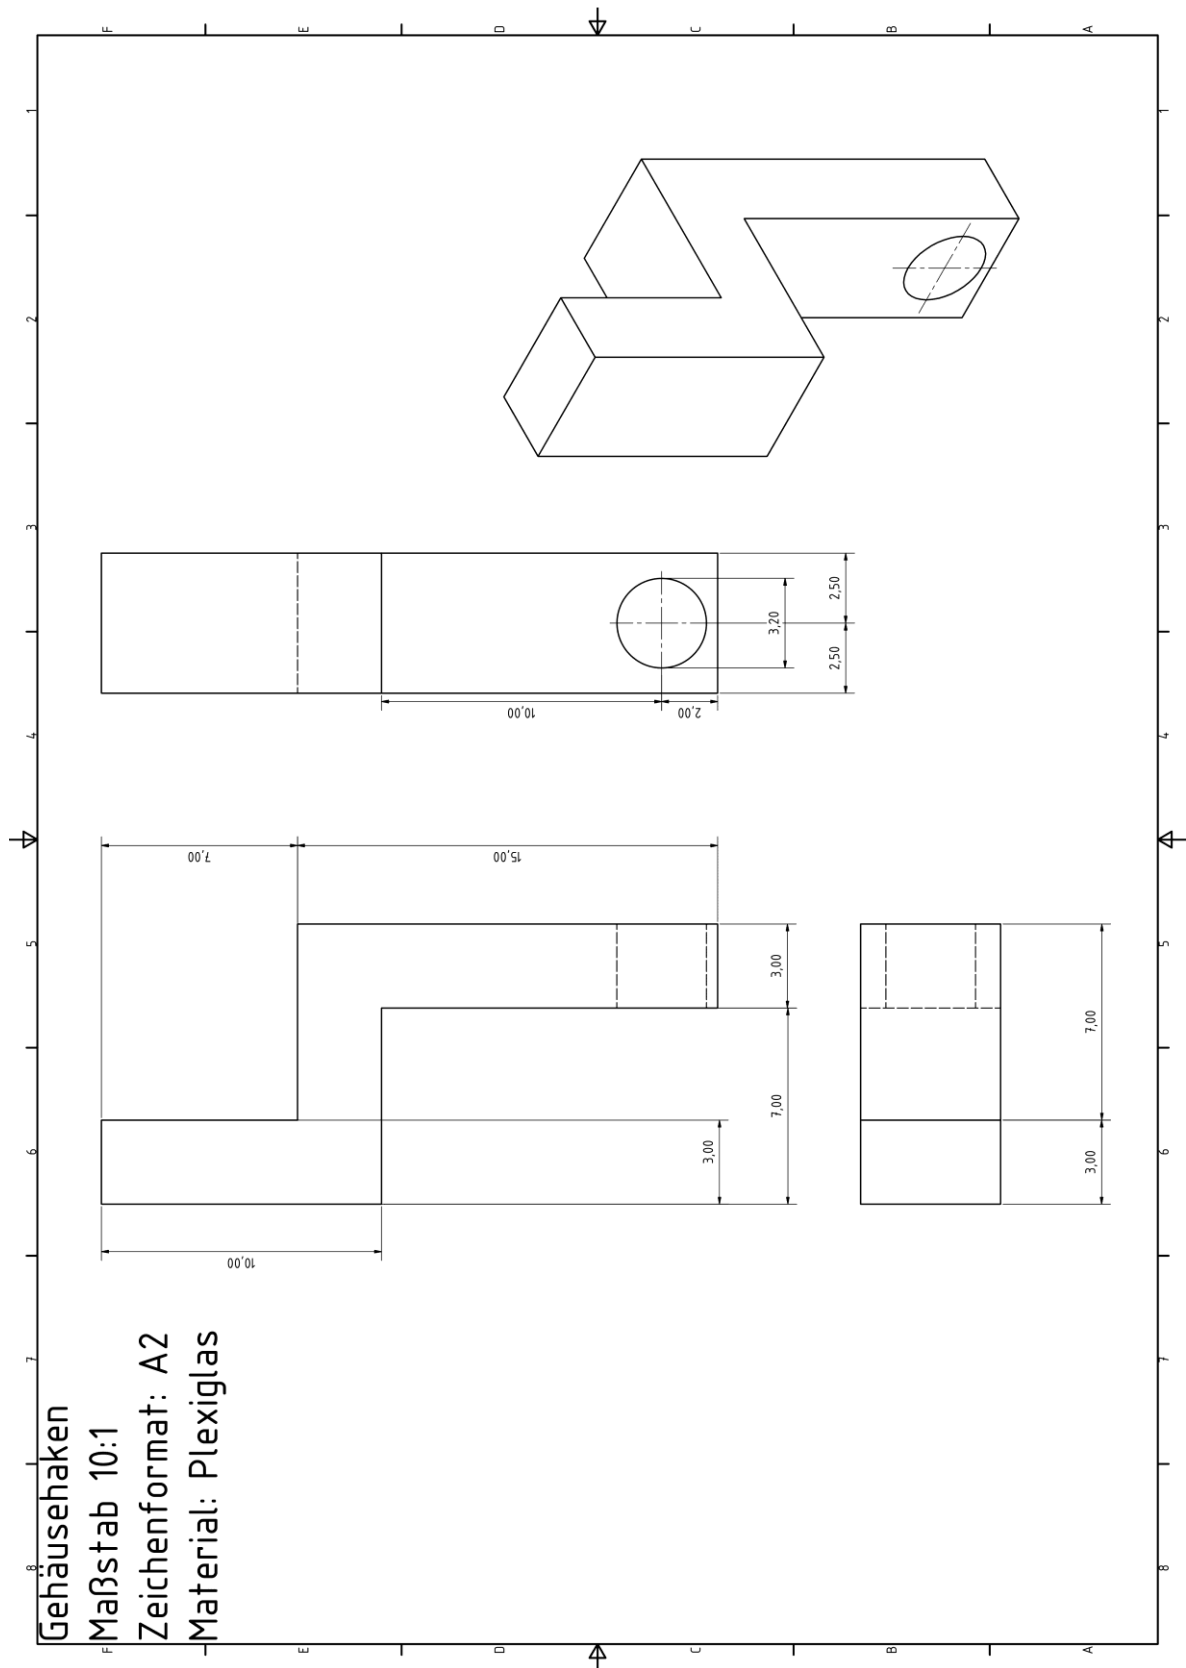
Konstruktionszeichnung Basissegment Gehäusehaken
